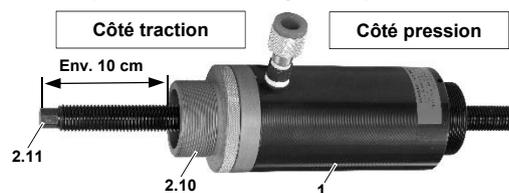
Visser le vérin hydraulique dans la plaque de base.
